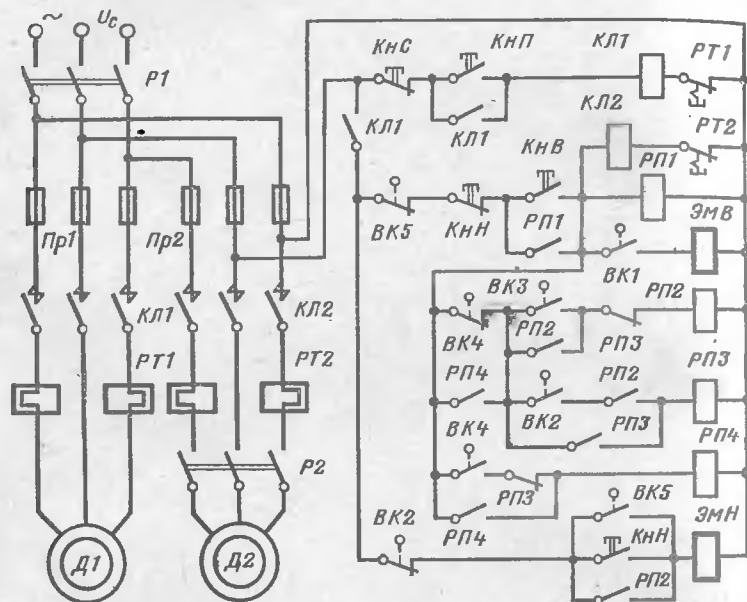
Электрическая схема управления агрегатным станком для глубокого сверления.
